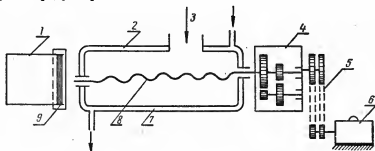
Схема шприц-машины для изготовления протекторной ленты:
